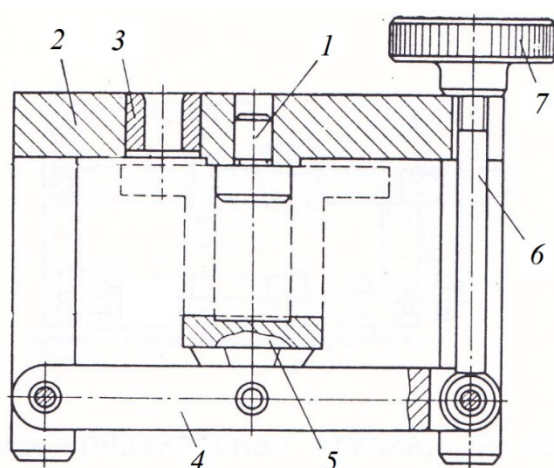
Пример крышечного кондуктора с откидной прижимной планкой:
